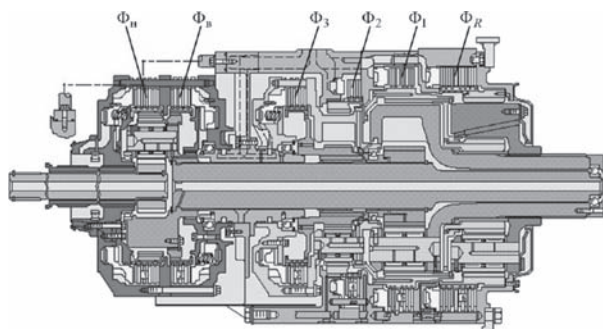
Конструкция коробки передач Caterpillar [10]
